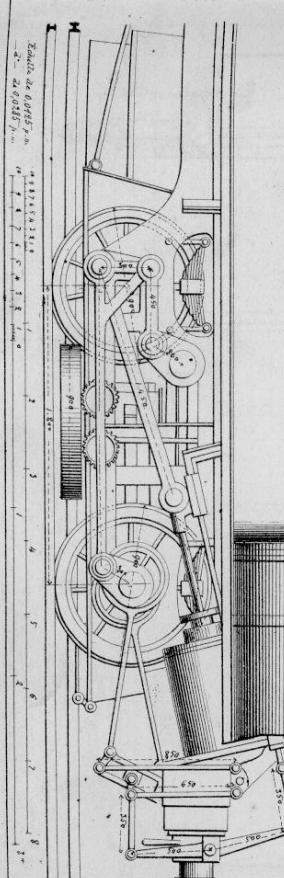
Elevation, coupe longitudinale à 0.021 p.m.
